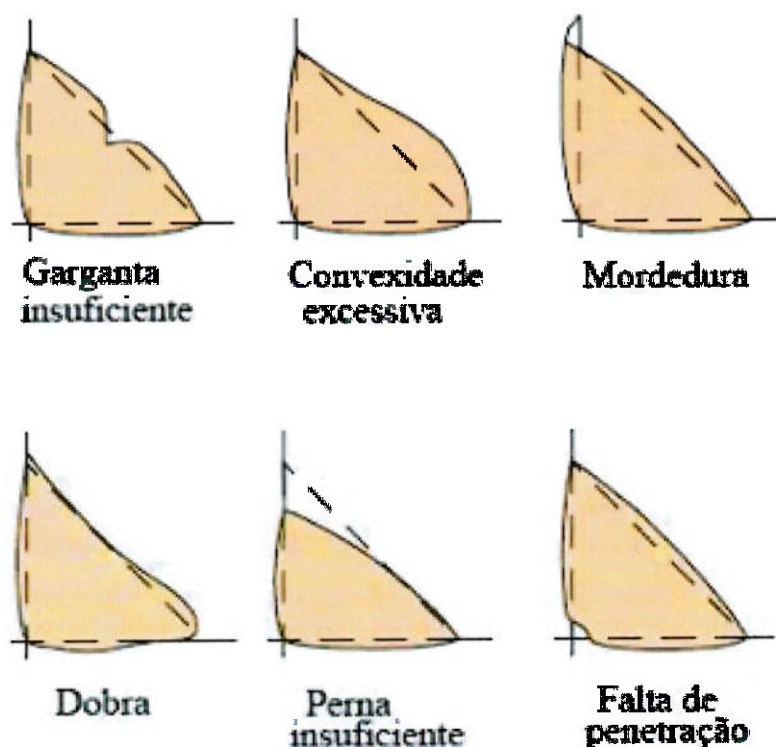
Alguns perfis de soldas inadequados. [9]
